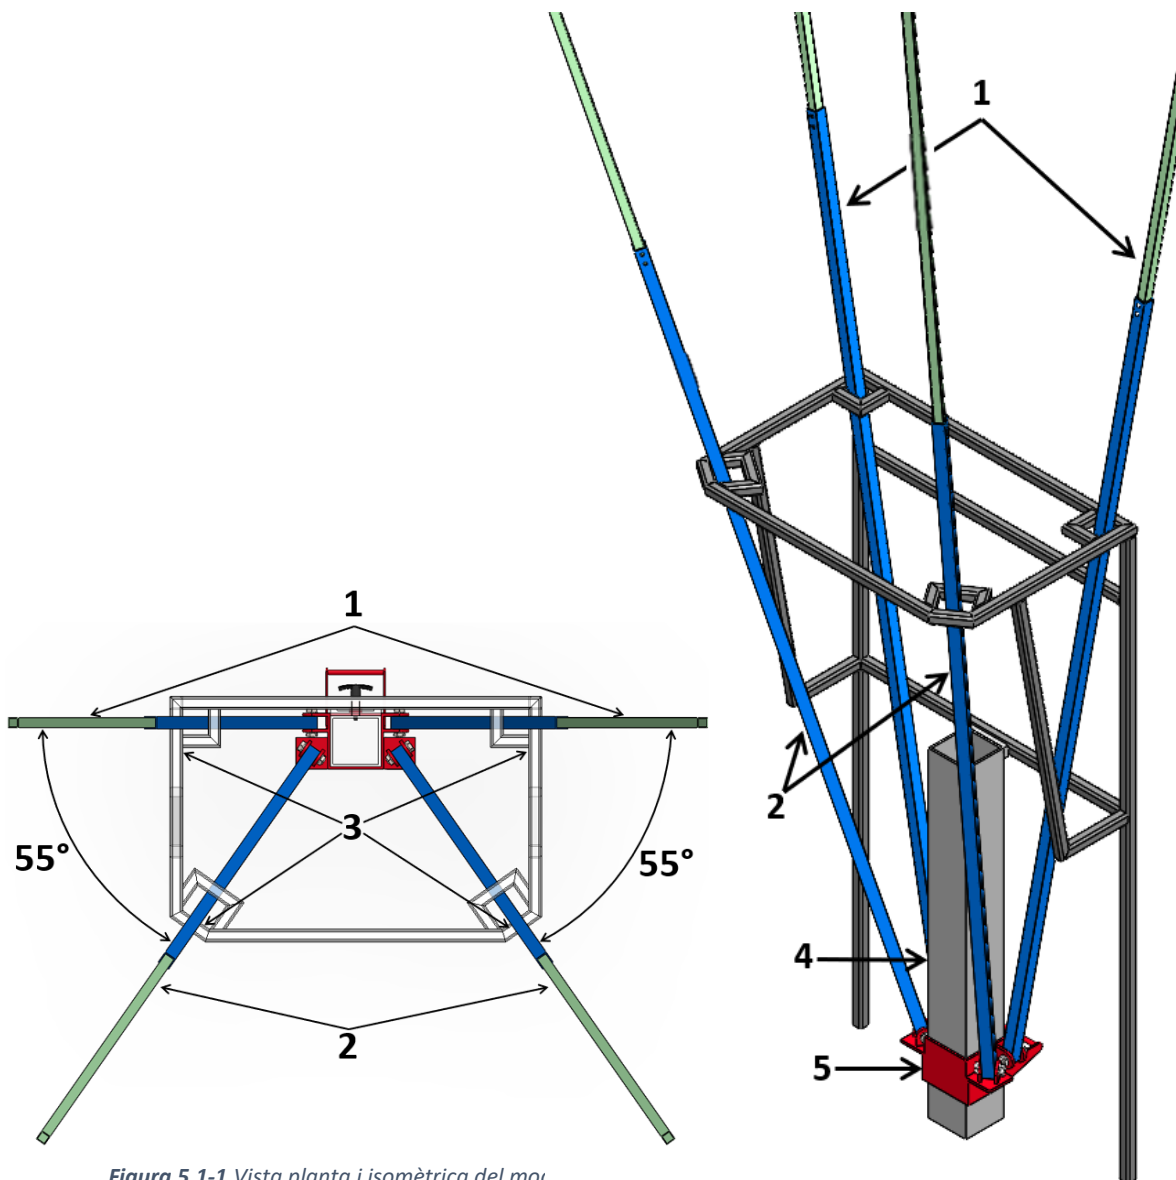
Vista planta i isomètrica del mecanisme
